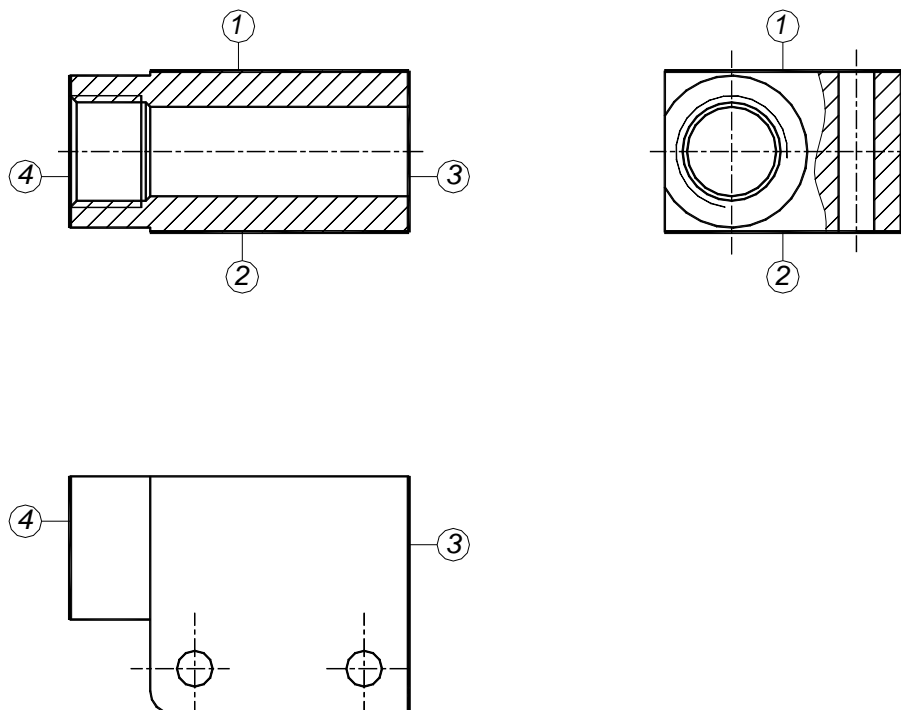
Поверхности, требующие фрезерной обработки
